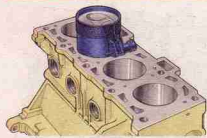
Установка поршня с поршневыми кольцами в цилиндр при помощи регулируемой втулки 67.7854.9519
